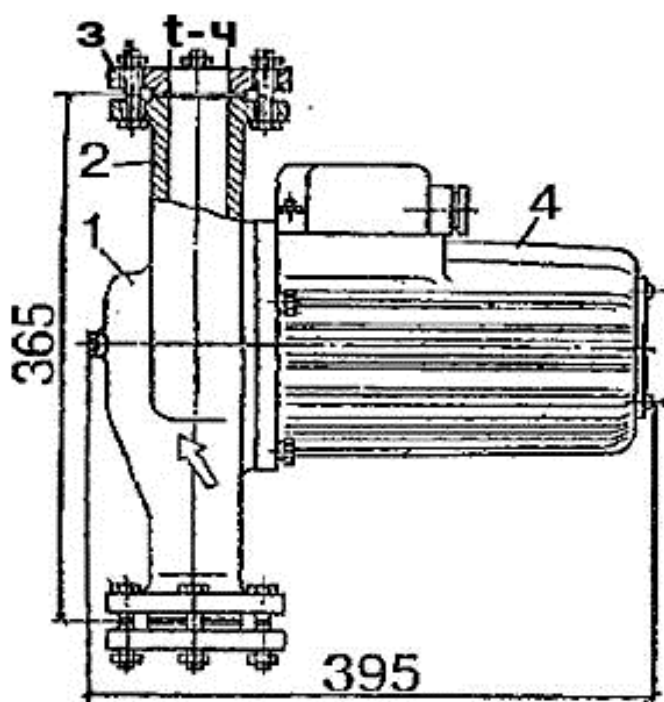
Центробежный циркуляционный насос типа ЦВЦ:
